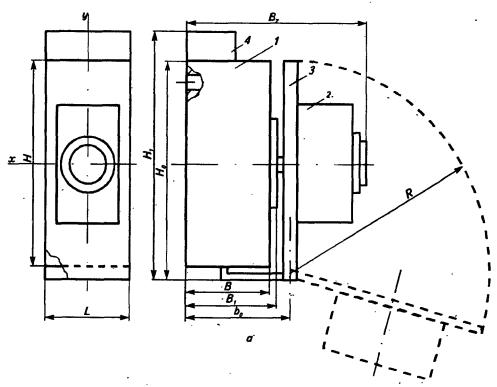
Габаритный чертеж выключателей стационарного исполнения с ручным приводом
